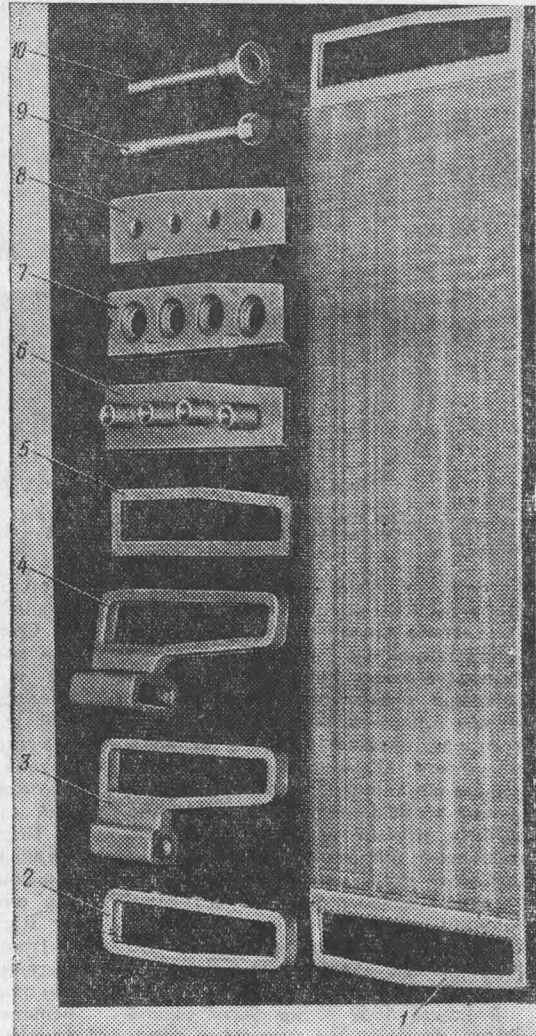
Детали алюминиевого радиатора АРСТ-31: 1 — секция; 2, 3, 4 — кольца коллекторные; 5 — паронитовая прокладка; 6, 7, 8 — коллекторные накладки; 9 и 10 — стяжные болты
